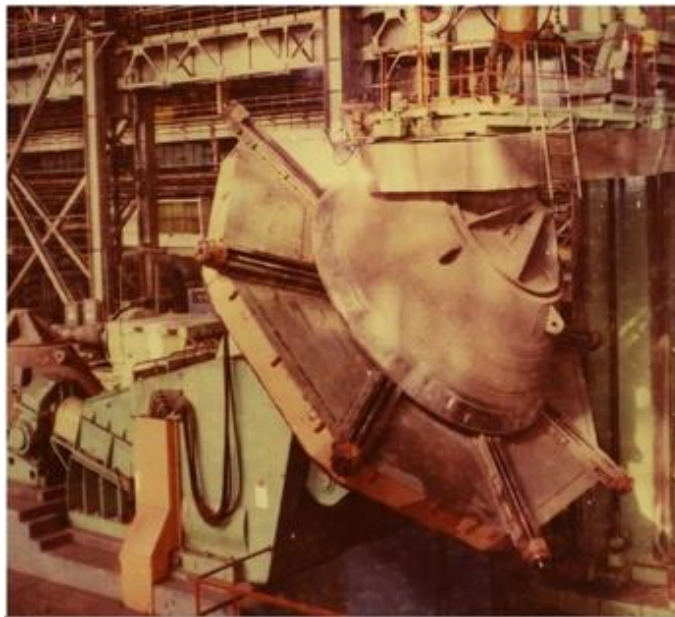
Установка для автоматичної наплавки У-50х7000
